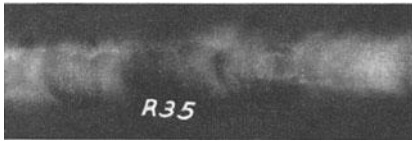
Röntgenbild (Positiv) einer schlechten Schweißung.
